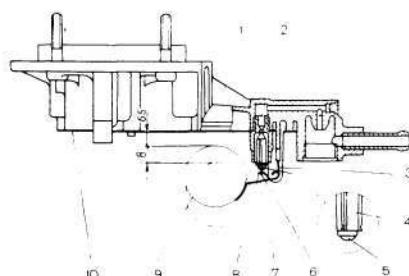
Установка уровня топлива в поплавковой камере карбюратора: 1 — крышка карбюратора; 2 — седло игольчатого клапана; 3 — упор; 4 — игольчатый клапан; 5 — шарик; 6 — оттяжная вилка; 7 — рычаг; 8 — язычок; 9 — поплавок; 10 — прокладка
